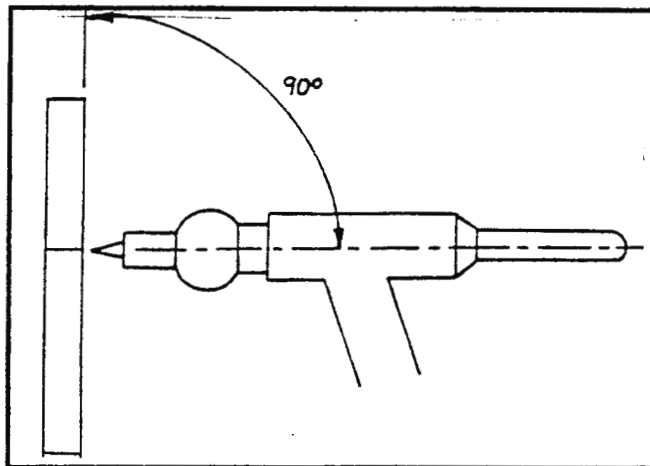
Posición de la pistola a las piezas a soldar vista de lado ángulo lateral
